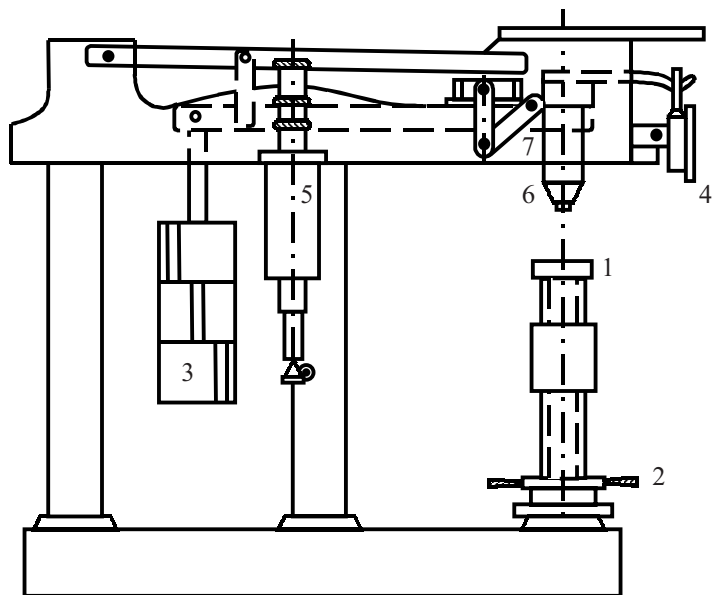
Схема прибора для измерения твердости по Роквеллу:
